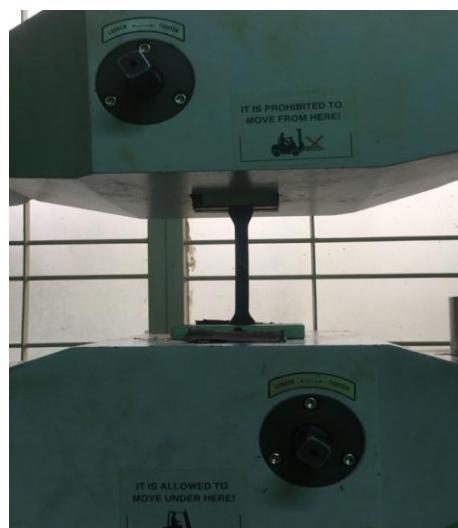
Universal testing machine (UTM) untuk pengujian tarik sambungan baja
